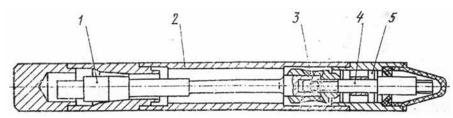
Вибронаконечник вибратора типа ИВ-117А 1 – бегунок; 2 – корпус; 3 – муфта резинометаллическая; 4 – шпиндель; 5 – подшипники.
